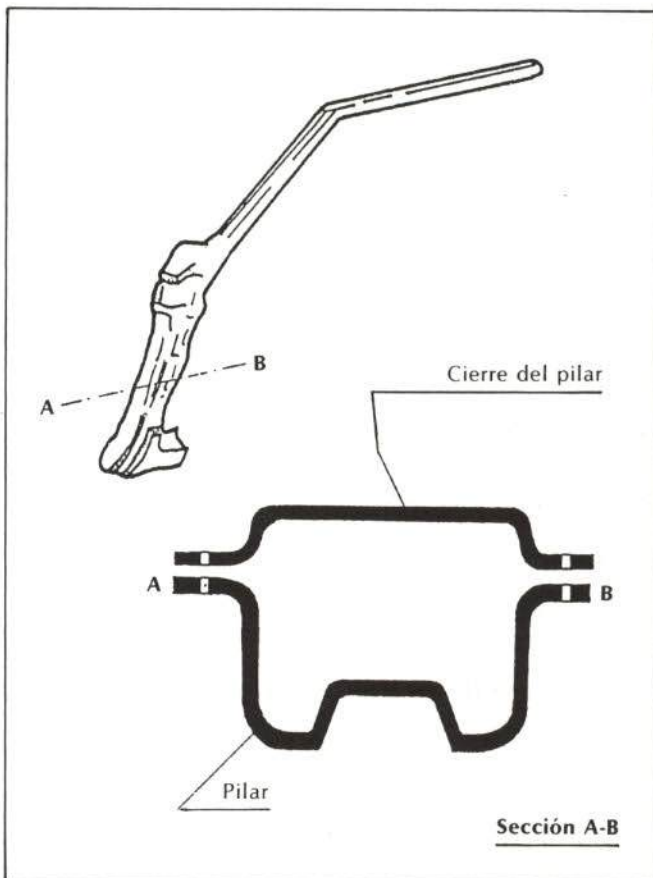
Accesibilidad. Sección del pilar delantero.
